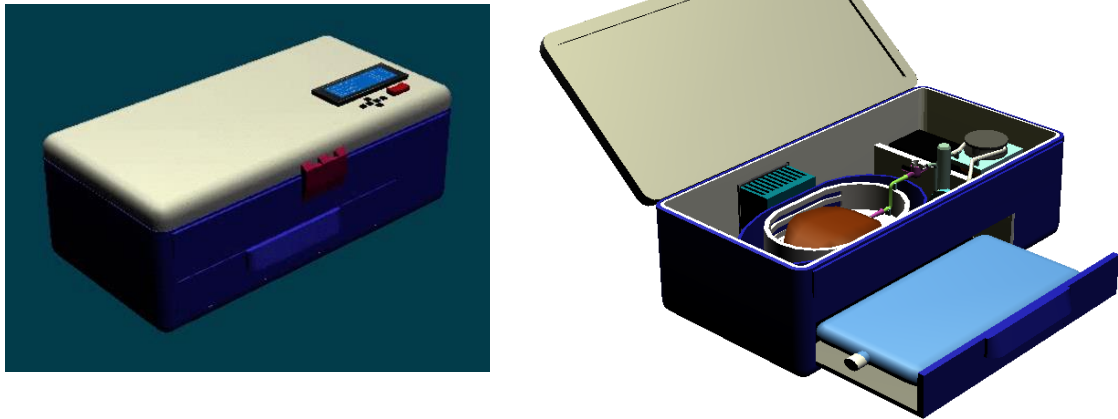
El diseño del equipo se realizó mediante tecnología CAD (*computer assisted design*), la cual no solo permite evaluar diferentes soluciones, sino que a su vez, constituye el primer paso para la fabricación de los componentes necesarios mediante impresión 3D.
